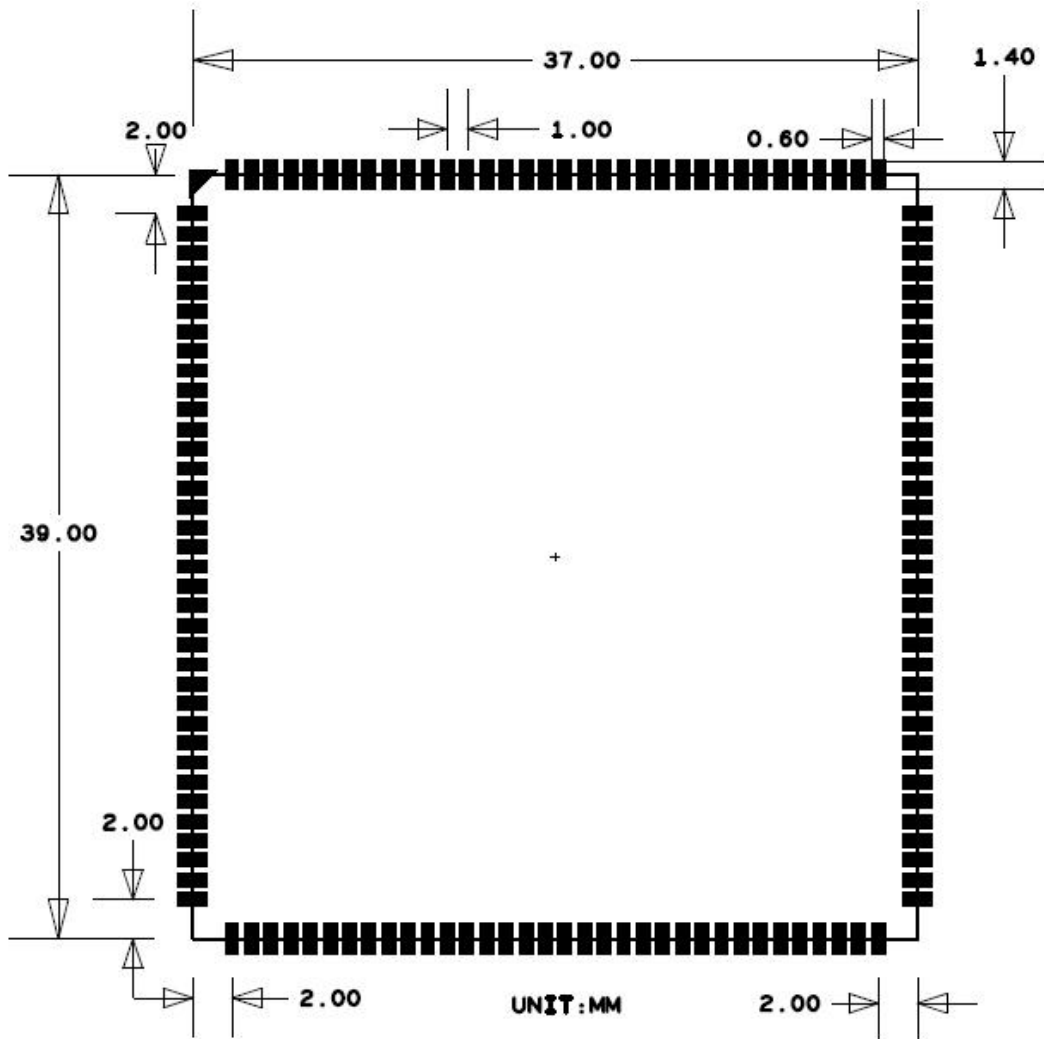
MYC-Y6ULX 推荐 PCB 封装
